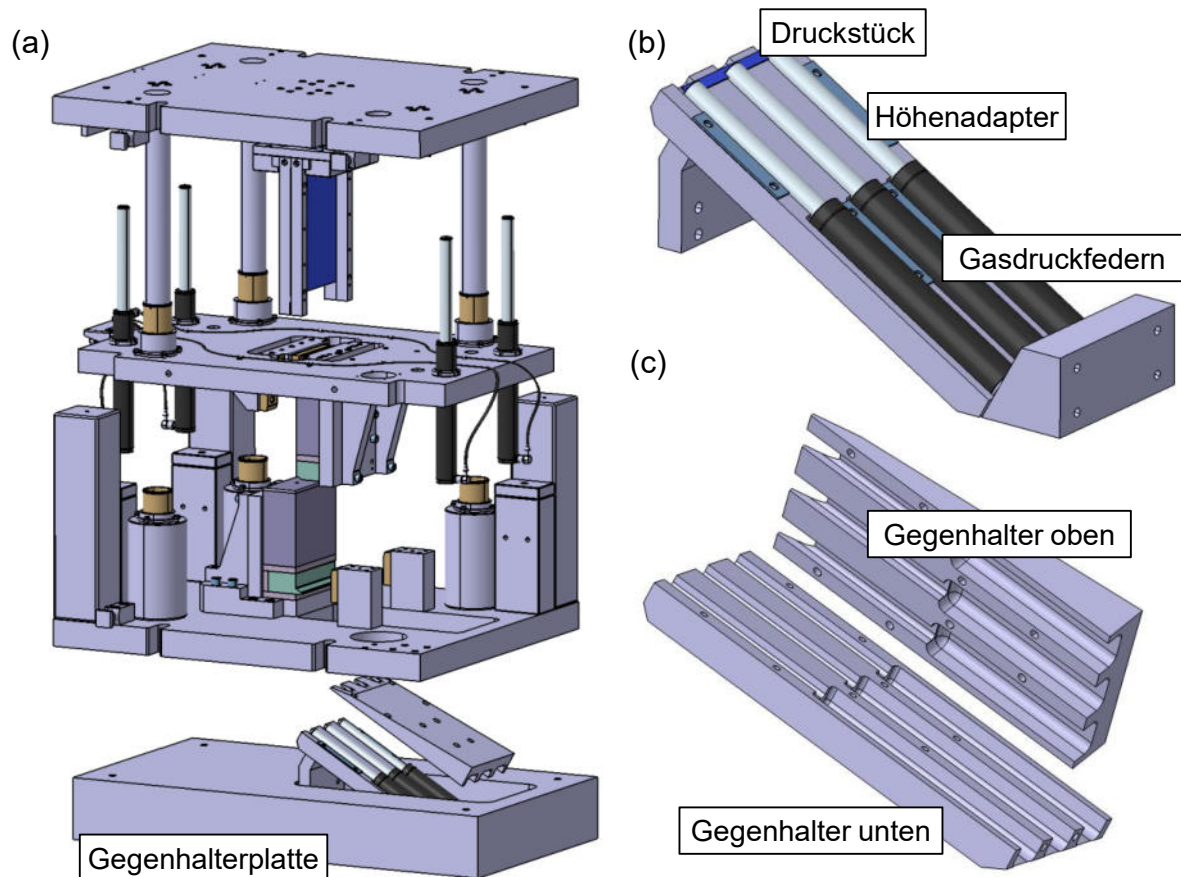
(a) Erweiterung des ECAP-Werkzeugs für Blechwerkstoffe um eine Gegendruckeinheit in einer Gegenhalterplatte, die von unten an das Werkzeug montiert wird; (b) Unterteil der Gegendruckeinheit mit Gasdruckfedern, Adaptern zur Anpassung der Kanalhöhe und dem Druckstück zum Aufbringen der Gegenkraft; (c) Kanalteile des Gegenhalters.
